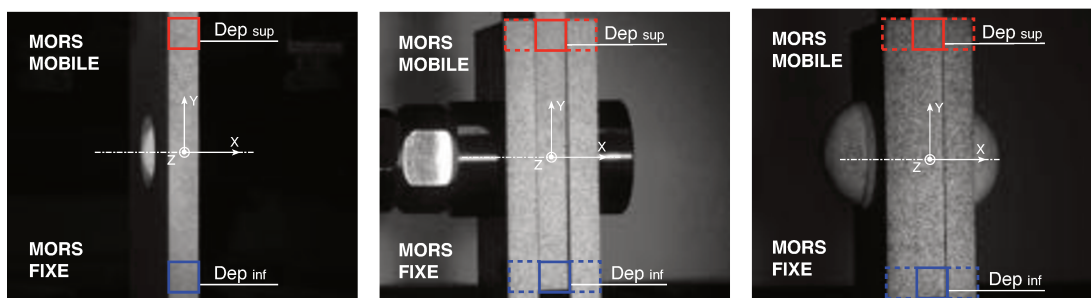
Exemple du mouchetis réalisé sur la surface latérale d'un assemblage riveté en acier.
